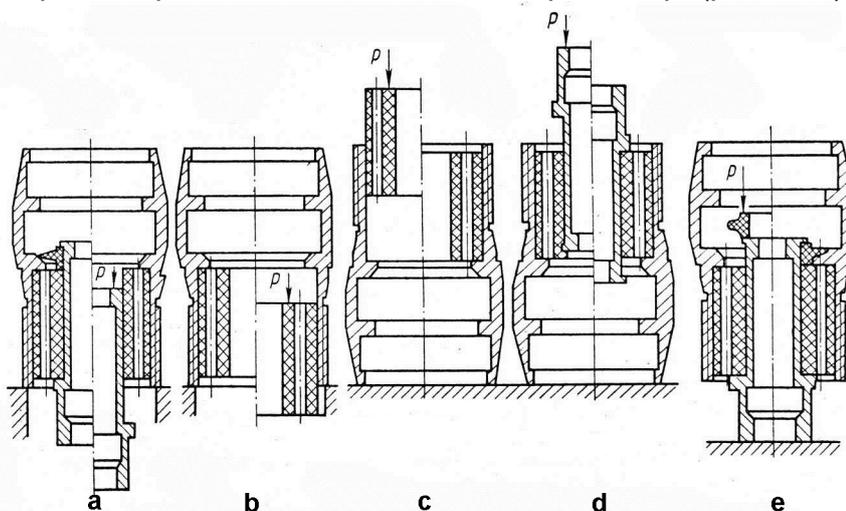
Схема выпрессовки – запрессовки деталей золотника
